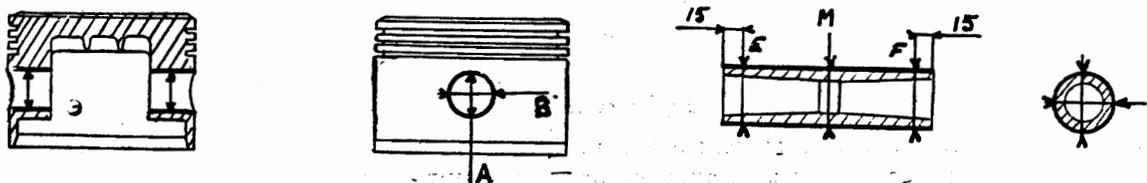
MENSURATIONS DES PISTONS ET AXES DE PISTON
